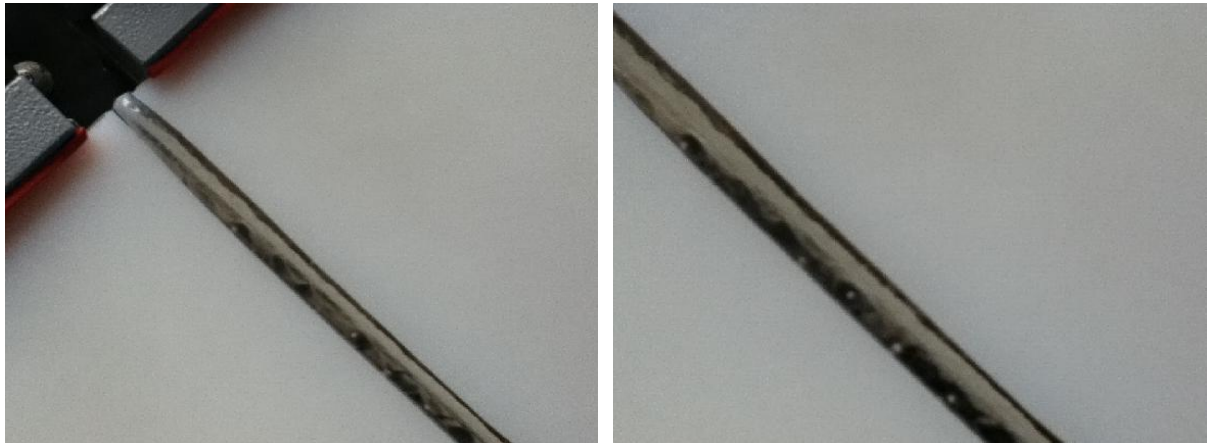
Unión de las zonas fundidas durante la soldadura.
